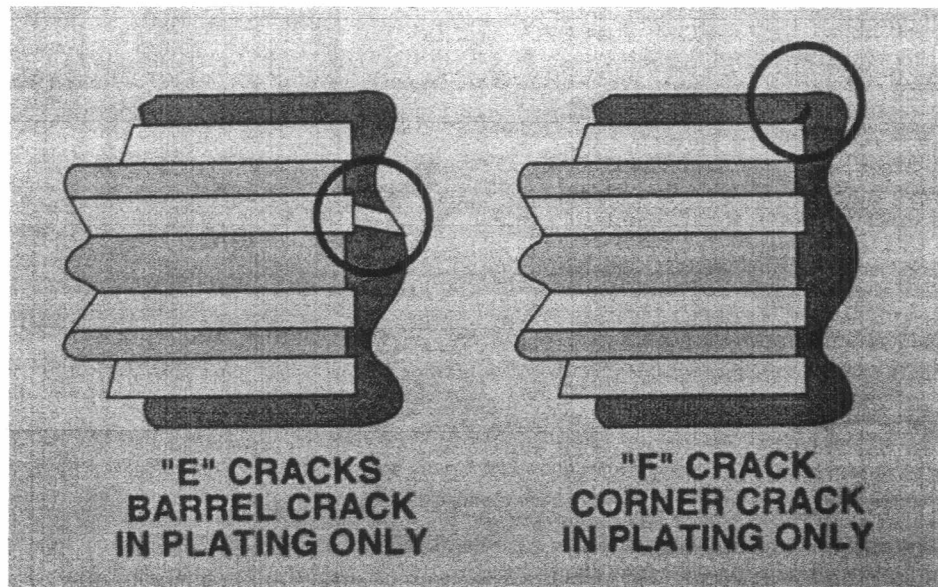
แสดงรูป Plated Through Hole ของ PCB
